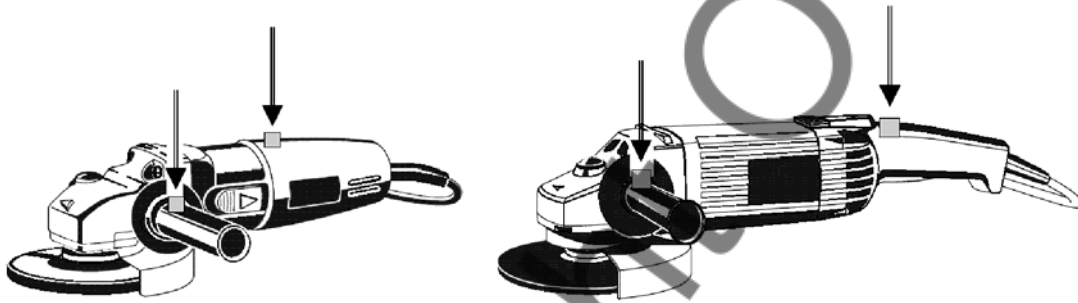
Lage der Schwingungsaufnehmer für Winkelschleifer
